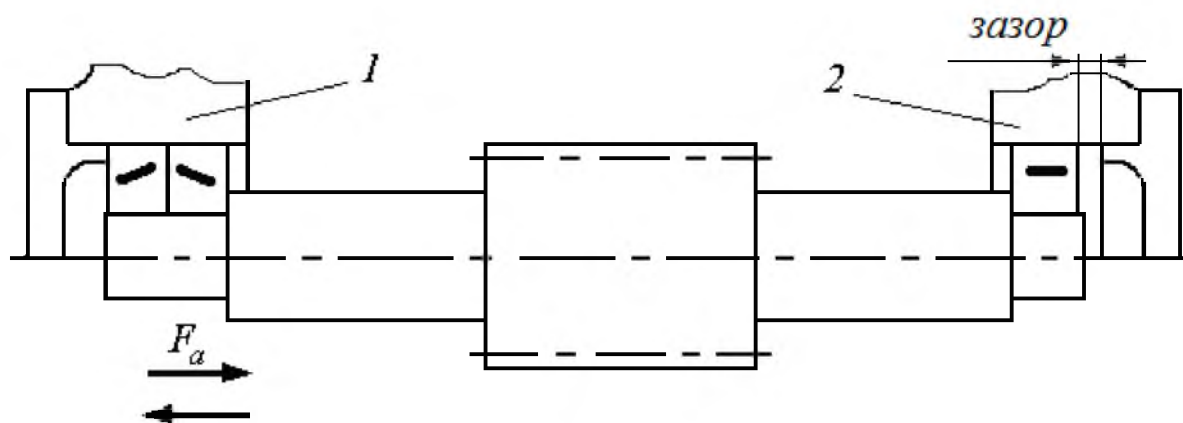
Установка червяка в опорах; опора 2 – плавающая
